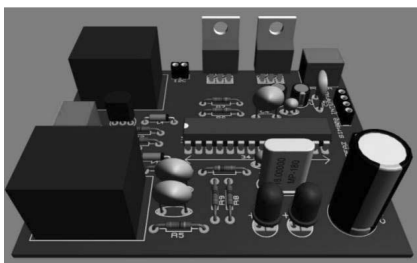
Diseño de la PCB mediante Proteus vista 3D.
